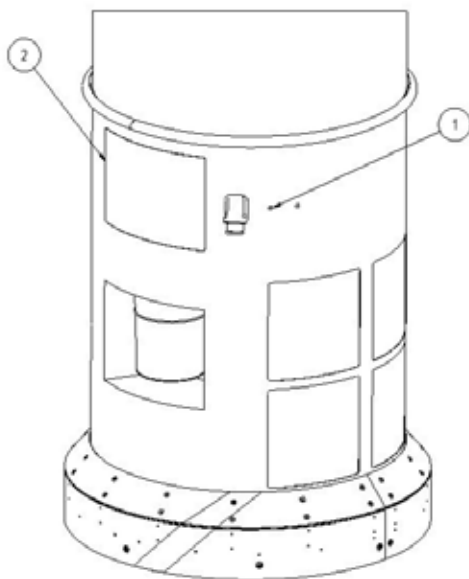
, слив конденсата из резервуара со сжатым воздухом
